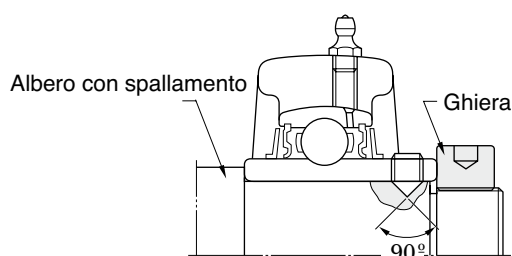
Esempio di installazione su albero con spallamento e ghiera di serraggio
